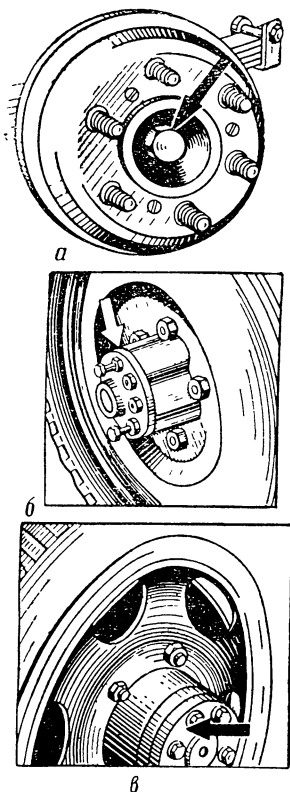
Точки смазки, смазываемые смазкой УТВ (смазкой 1-13):
